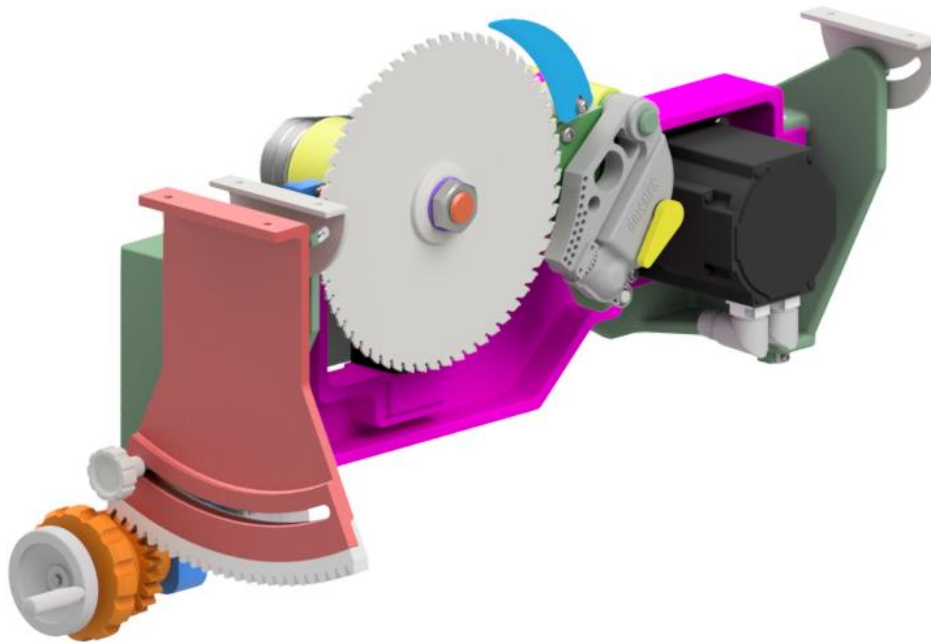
Řemenový převod ve sklopeném stavu
